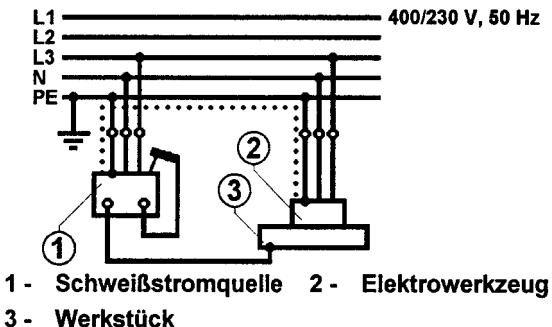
Der Schweißstrom fließt über die Schutzleiter des Elektrowerkzeuges und der Schweißstromquelle, wenn Stabelektronenhalter oder Lichtbogenbrenner Kontakt mit dem Schweißstromquellengehäuse bekommen.
